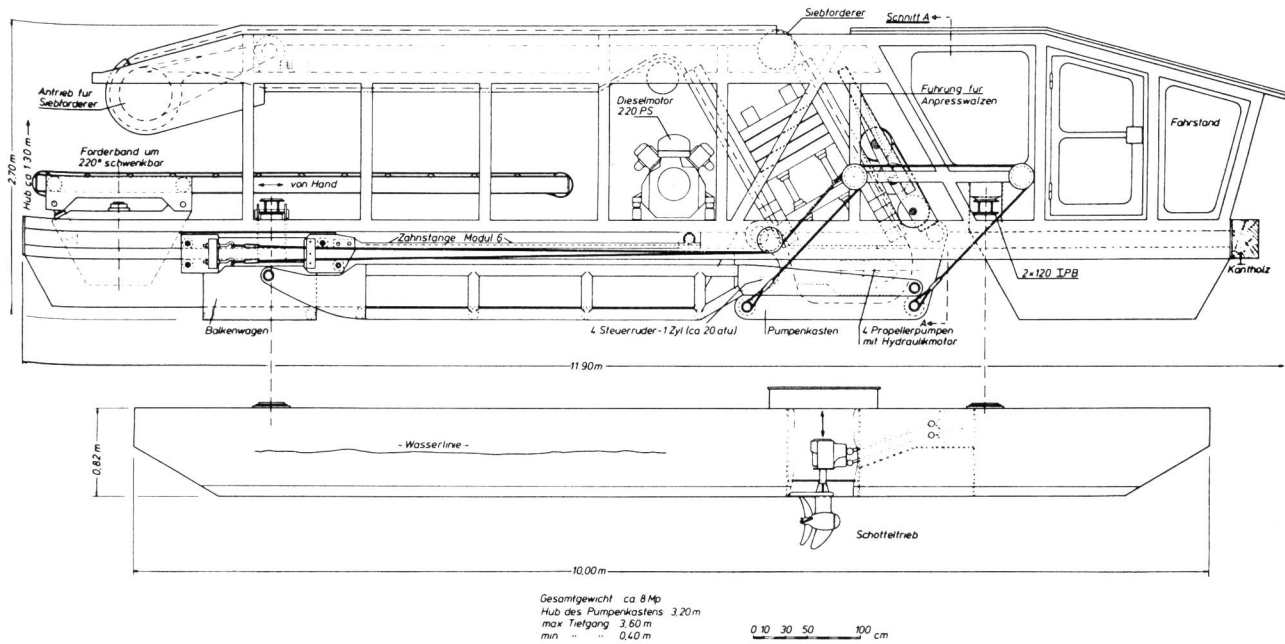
Wasserpflanzenentfernungsmaschine. Seitenansicht mit eingefahrenem Siebförderer.
